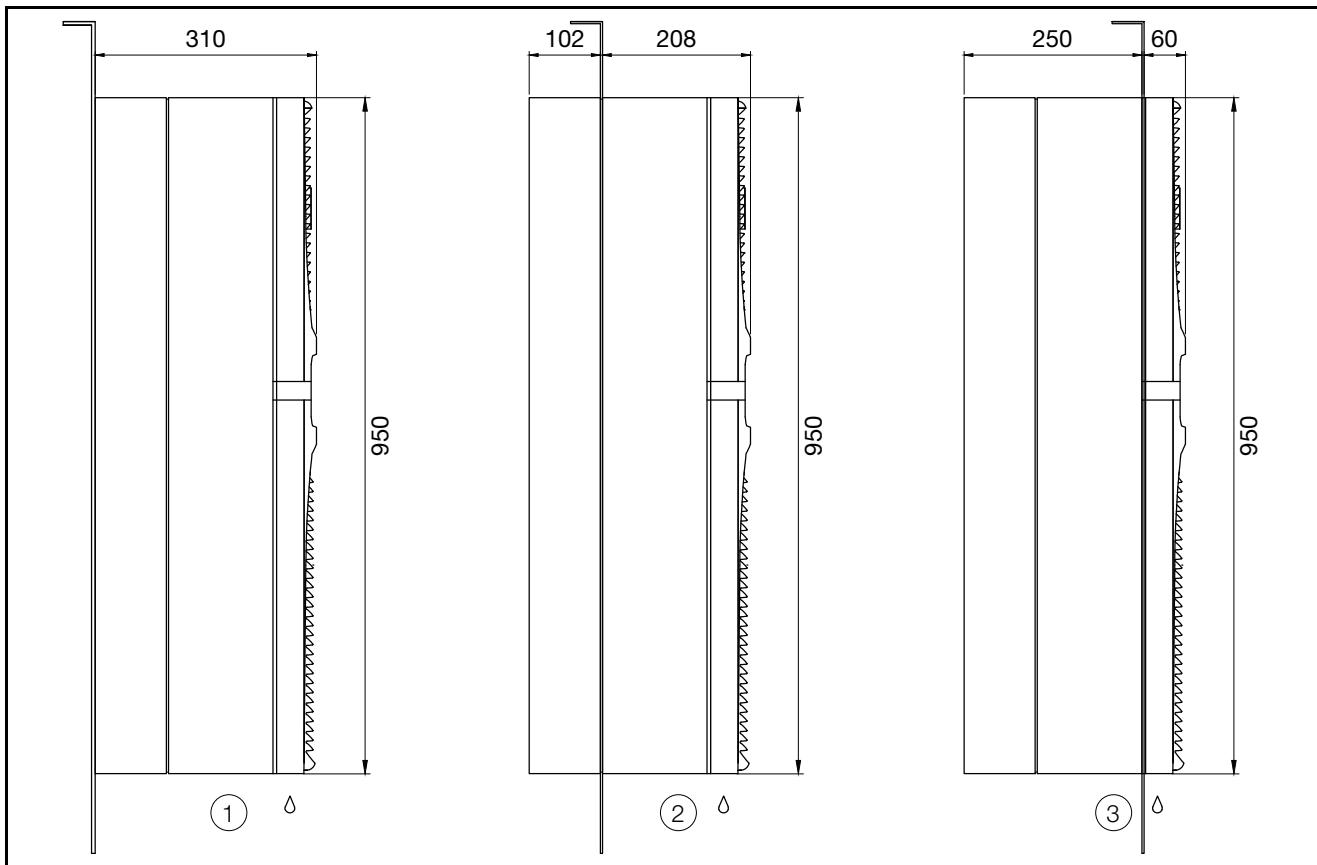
dimensions SK 3184837 et SK 3185x3x
